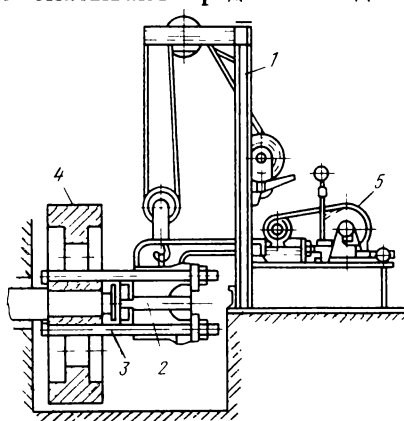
Переносной ремонтный пресс для запрессовки и распрессовки деталей
